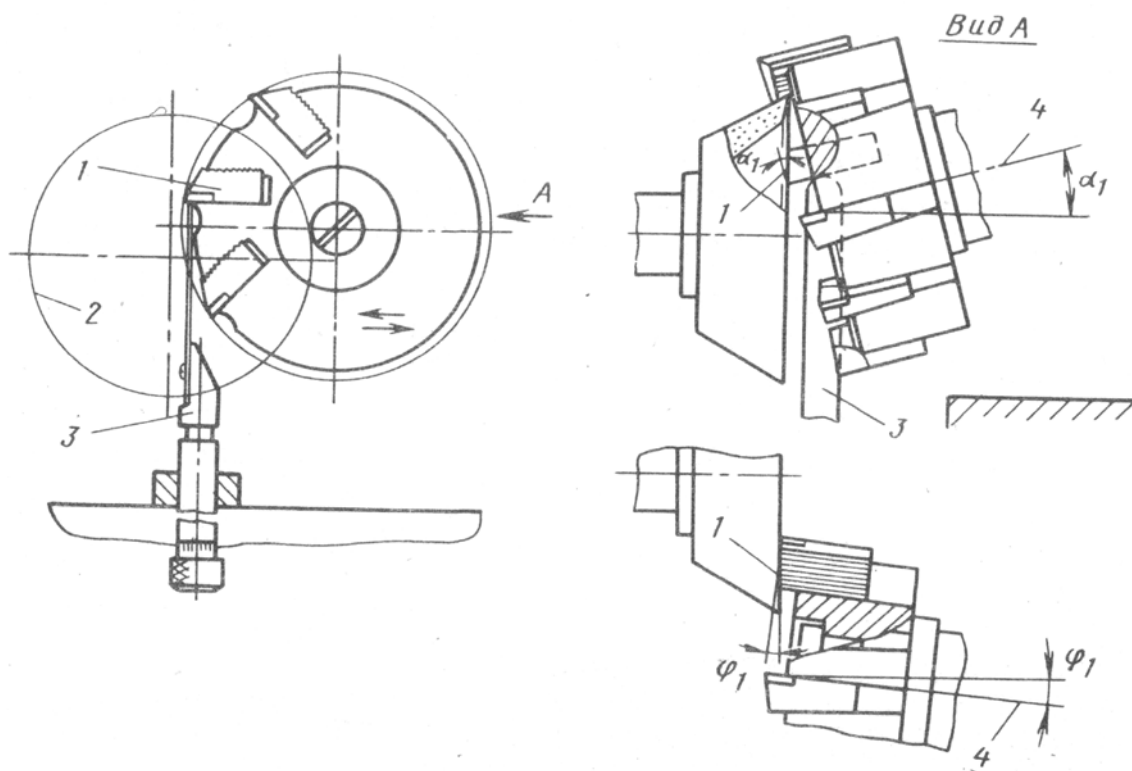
Схема установки фрезы для образования вспомогательных задних поверхностей:
